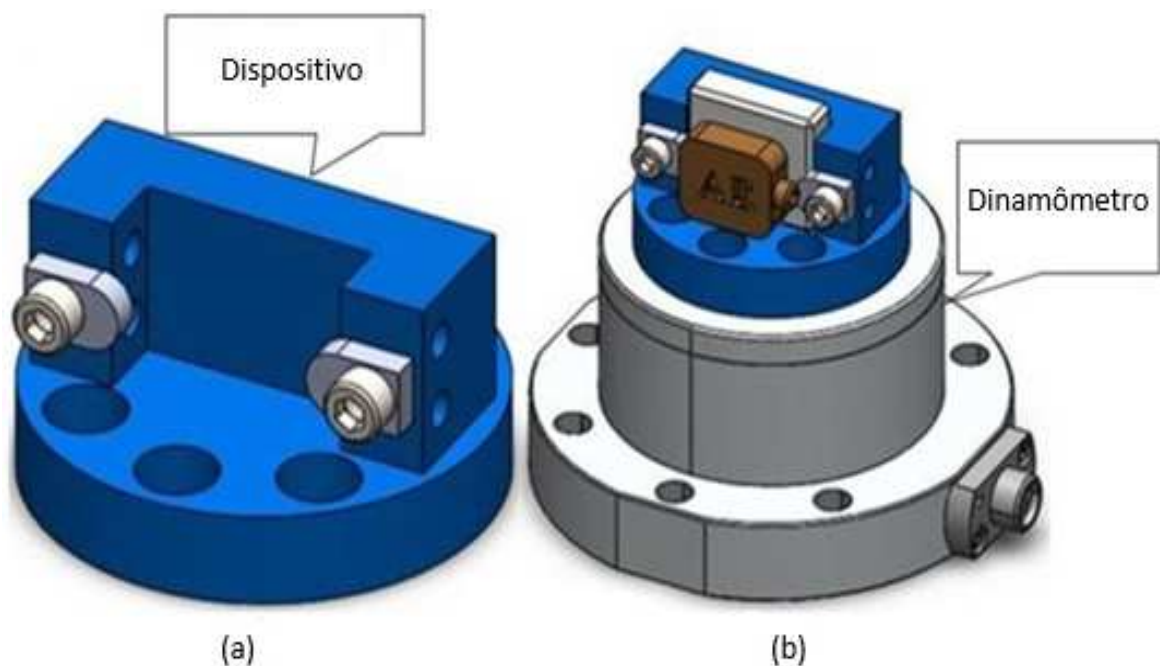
(a) Desenho 3D do dispositivo projetado para o microfresamento, (b) montagem 3D com o dinamômetro, emissão acústica, dispositivo e corpo de prova.
